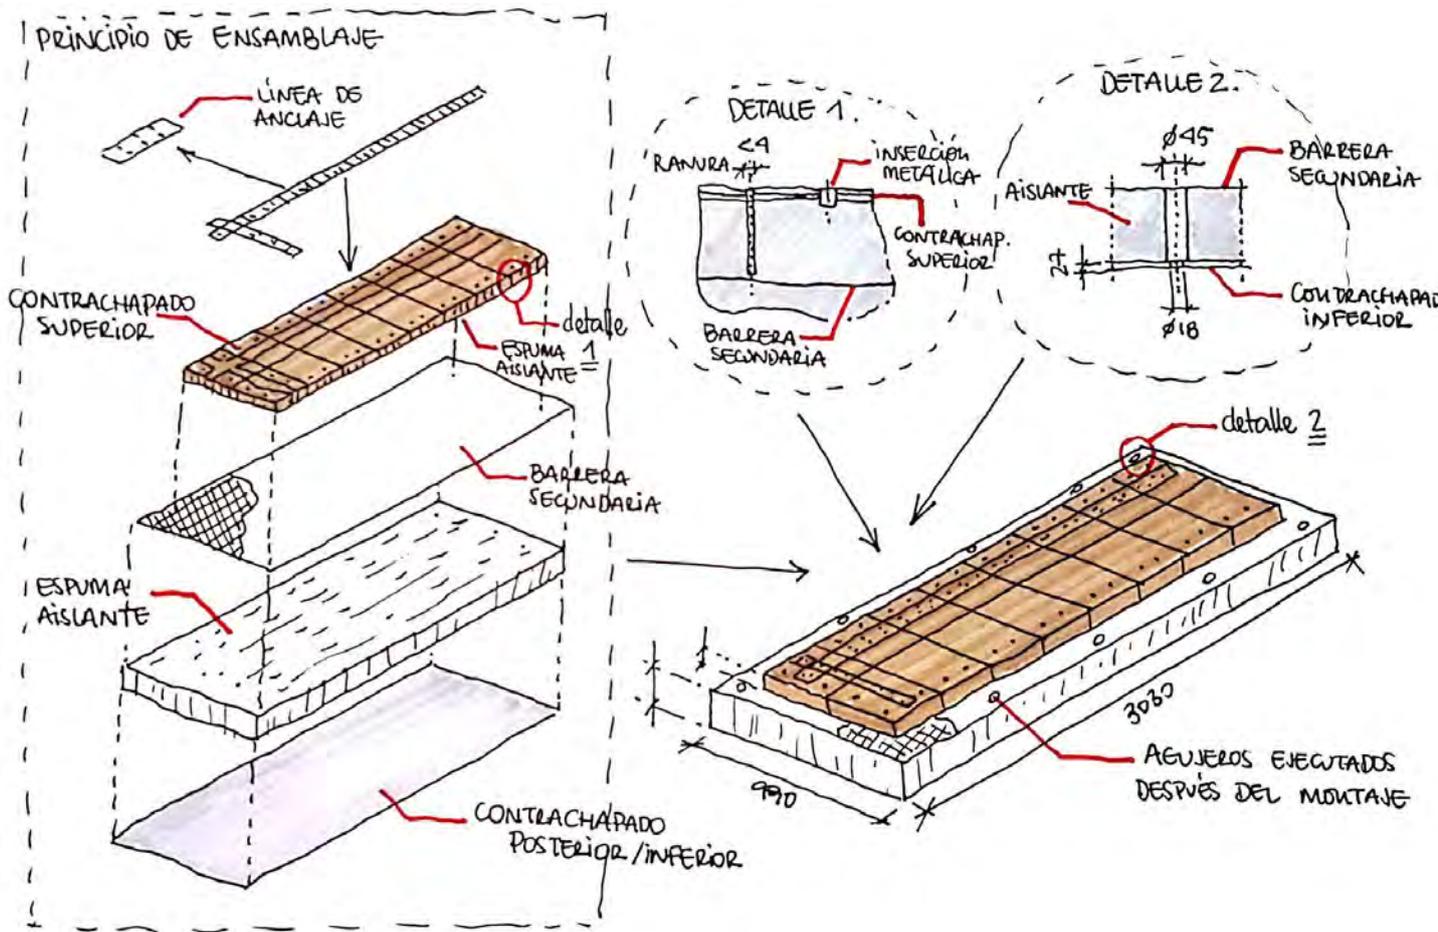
Detalle constructivo del principio de ensamblaje. Fuente: elaboración propia
